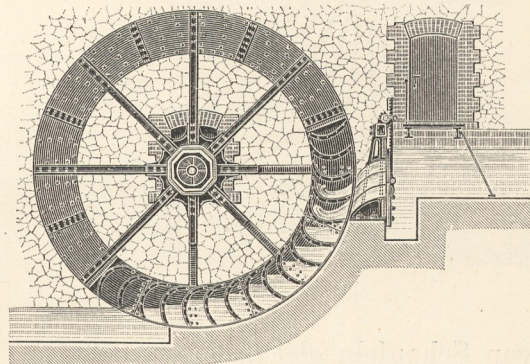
Mittelschlächtiges Wasserrad der Merseburger Maschinenfabrik Herrich &amp; Co. im Schnitt dargestellt.
